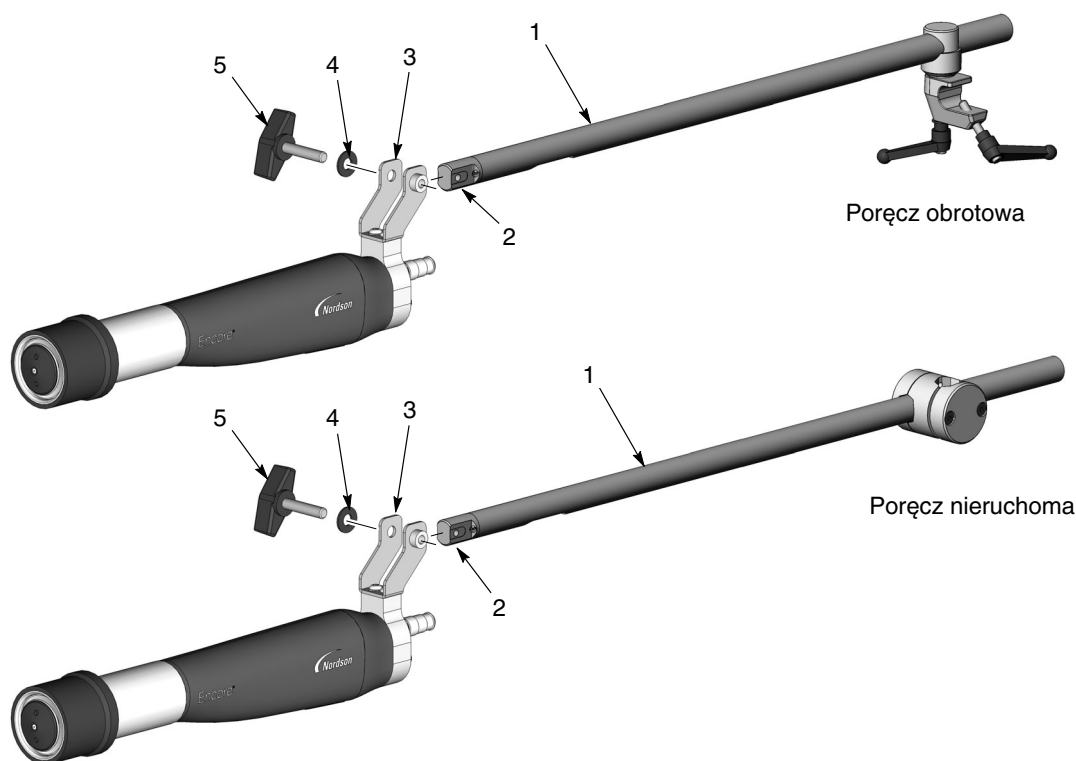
Montaż pistoletu mocowanego na standardowym obrotowym uchwycie do poręczy
